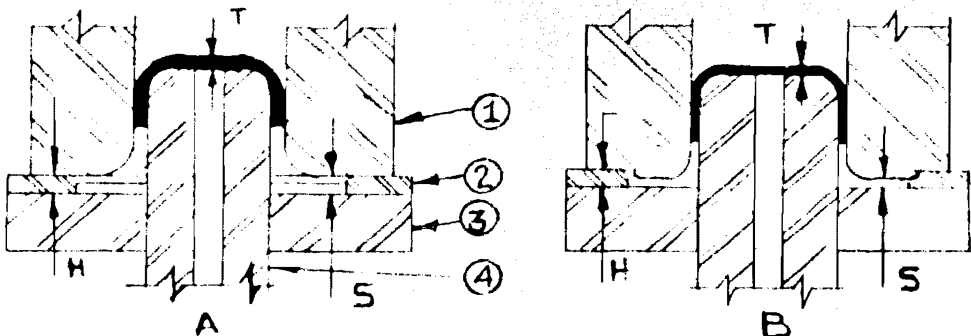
Los principales componentes del troquel son: (1) matriz, (2) Guía, (3) Pisador, (4) Punzón.
